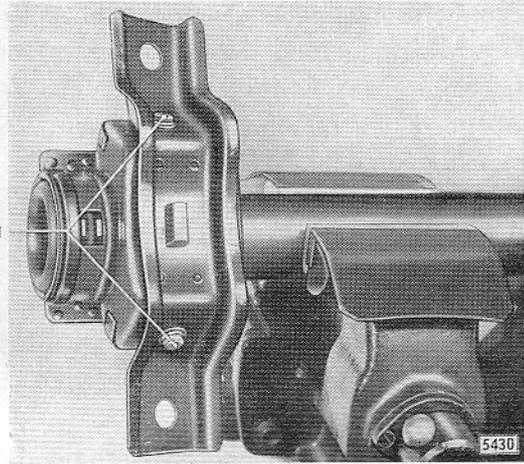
Gelenkbrücke an Gummipuffern der Hinterachsverlängerung befestigt
